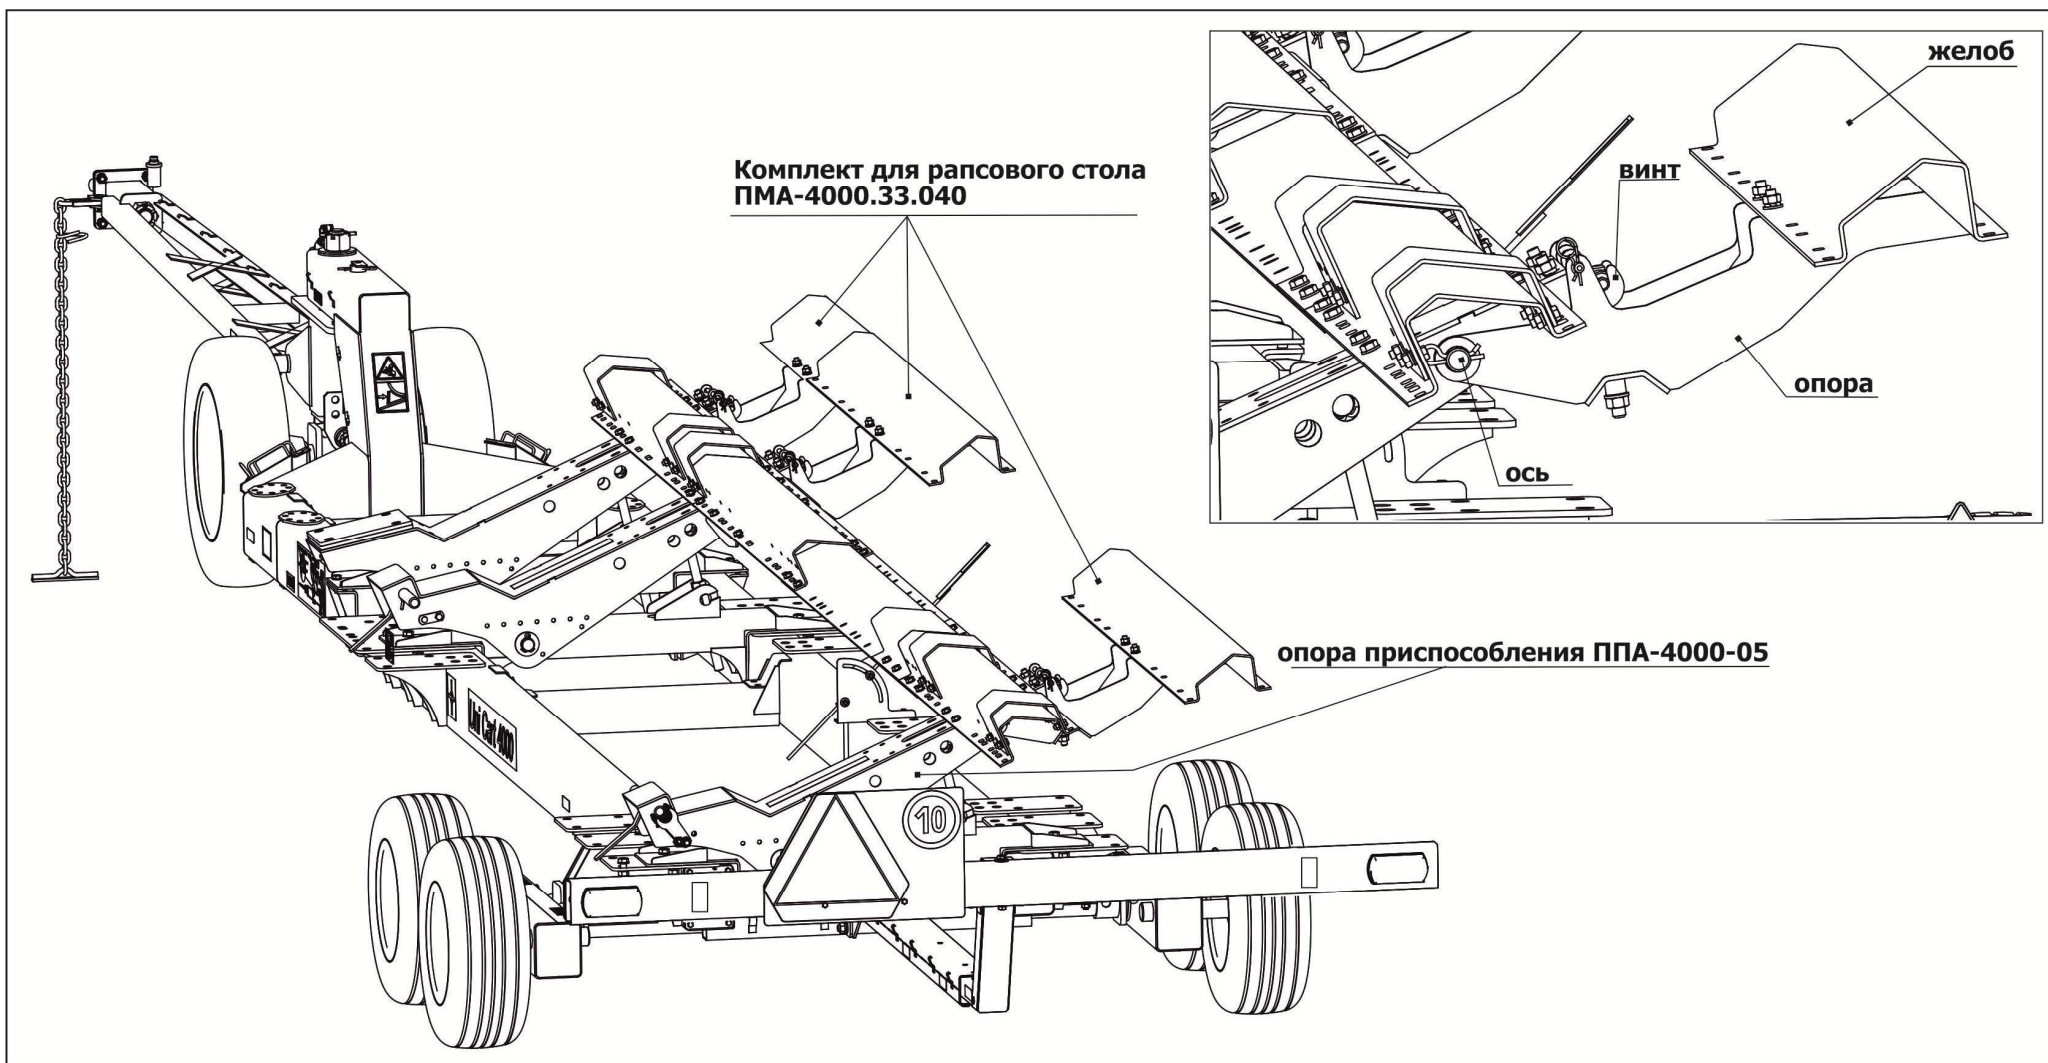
Установка комплекта для рапсового стола ПМА-4000.33.040 на приспособление ППА-4000-05
